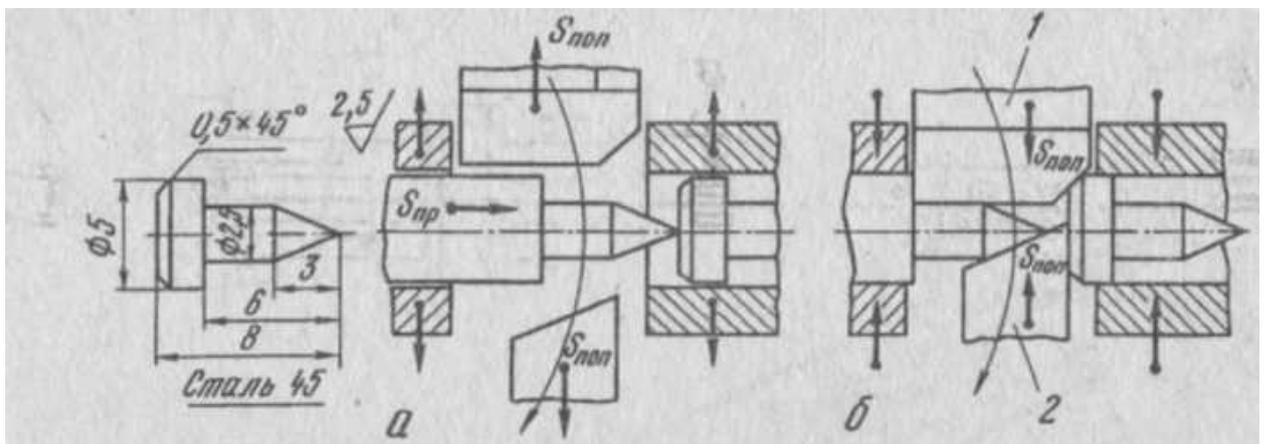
Схема обработки заготовки на фасонно-отрезном автомате: а – разжим и подача проволоки, б – зажим и обработка заготовки.
